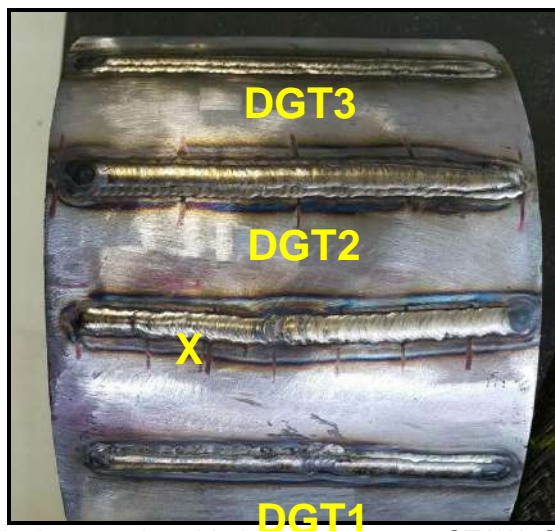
Cordões de dupla camada soldados por processo GTAW. O cordão identificado com X foi descartado.
